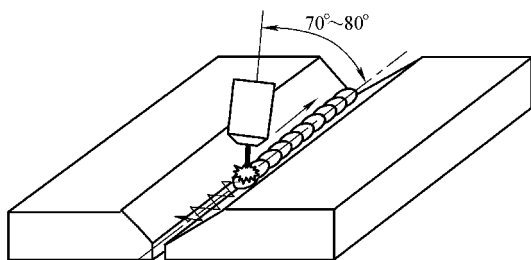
大坡口角度和间隙厚板的左焊法
